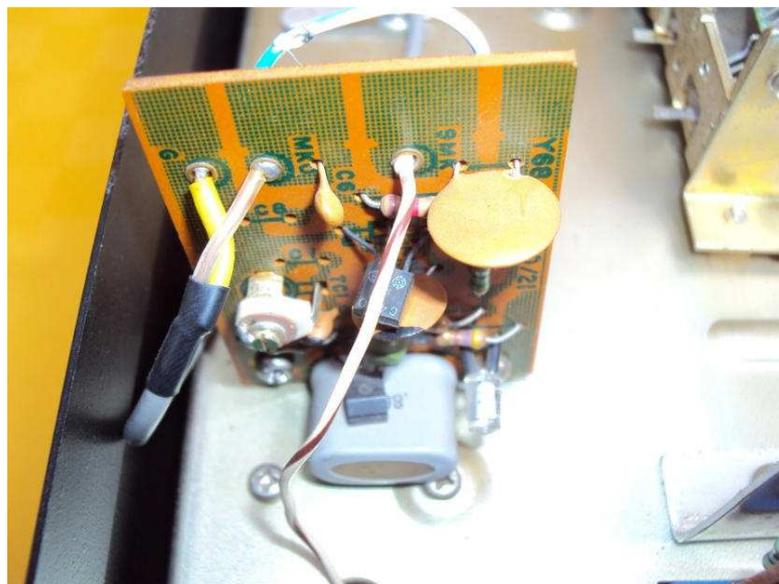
trasformatore di alimentazione con la scheda di BF e stabilizzazione
